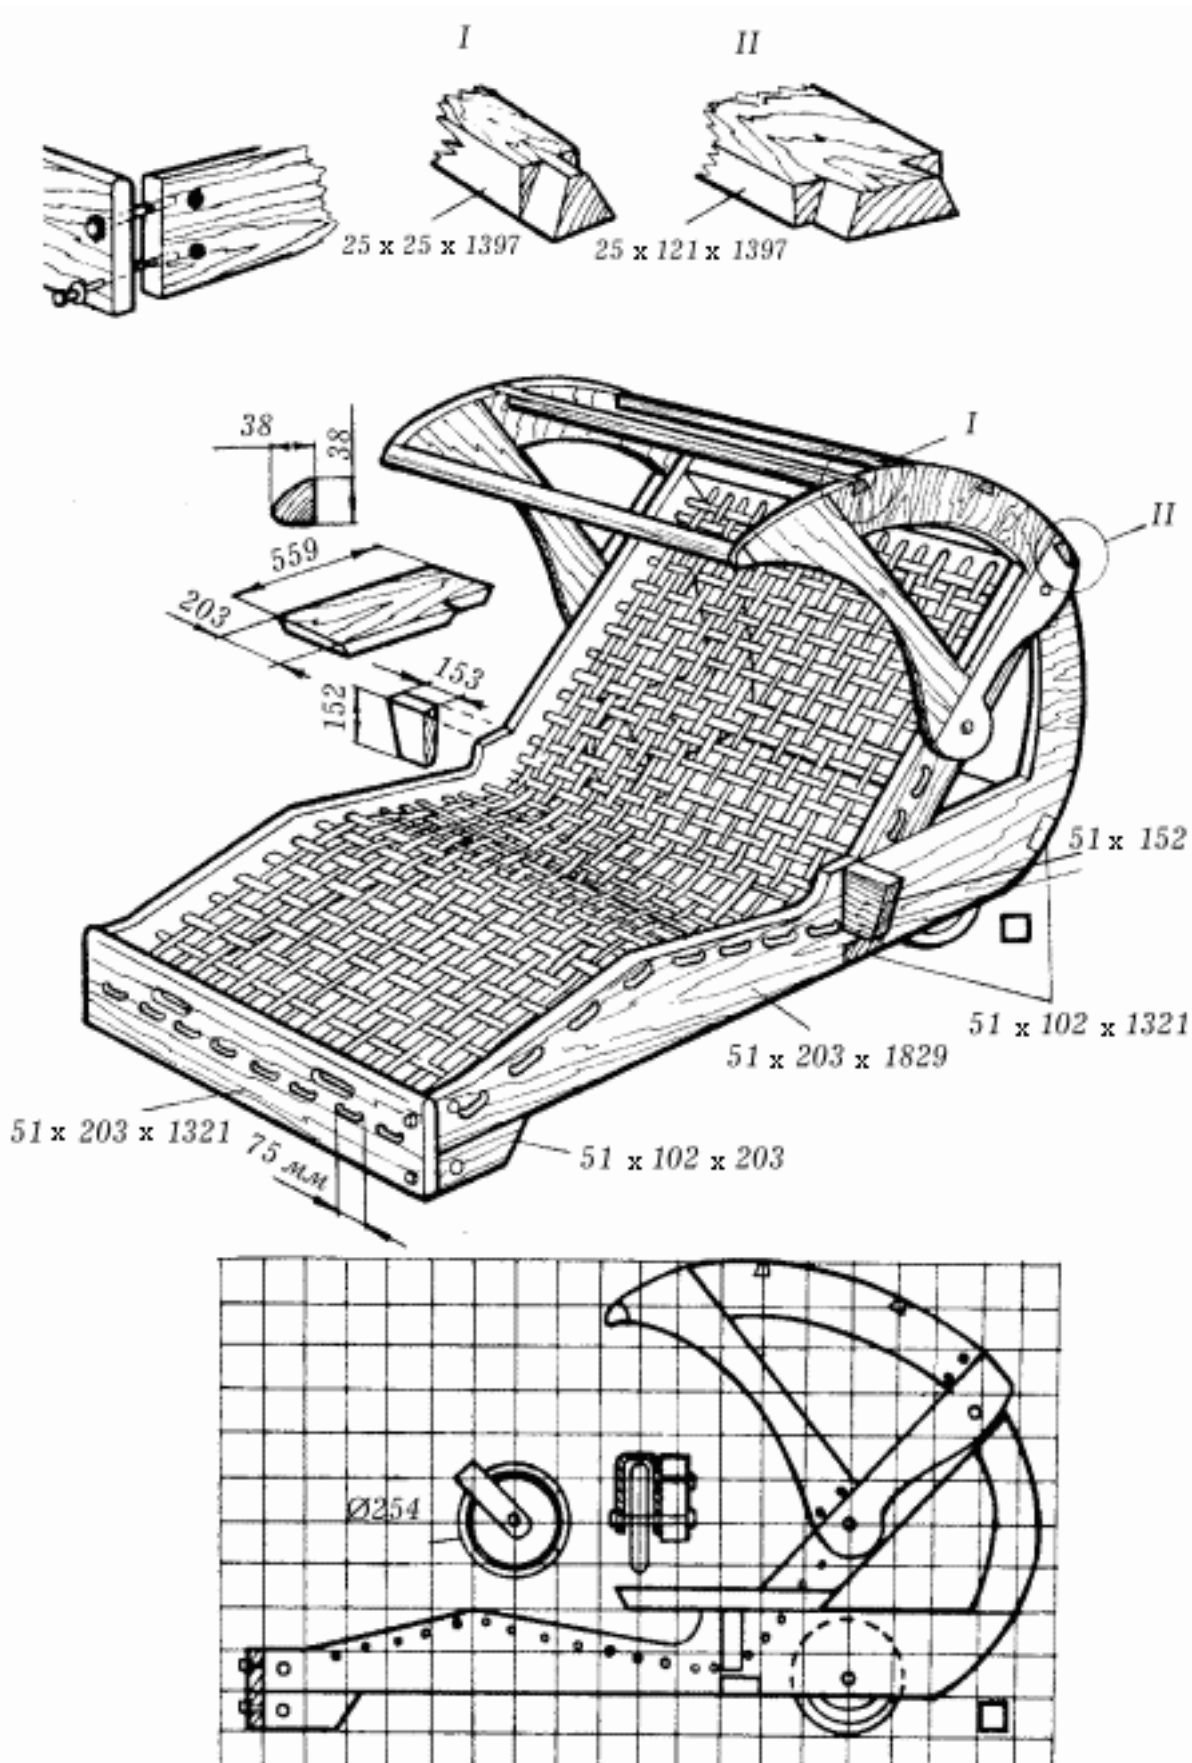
Садовый шезлонг: общий вид, детали сборки и шаблон для изготовления деталей с размером клетки 100 мм.
